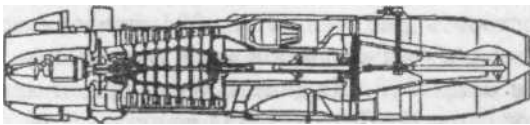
Турбореактивный двигатель Jumo-004 [59]
